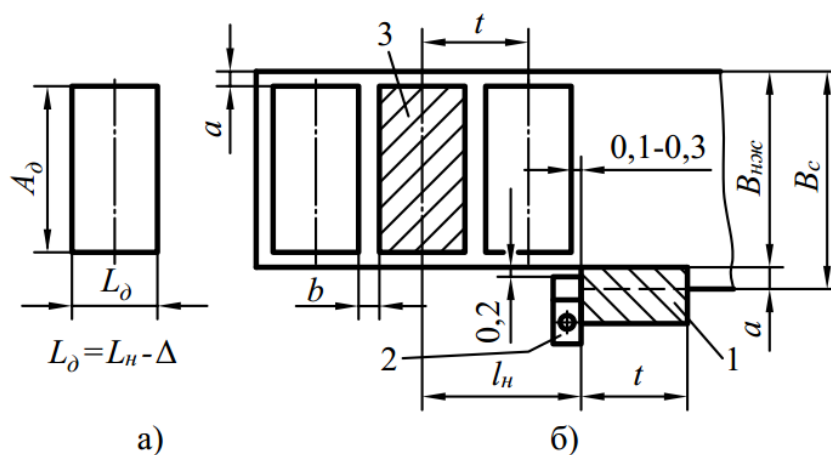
Схема вирубкування заготовки в штампі з кроковим ножом:
